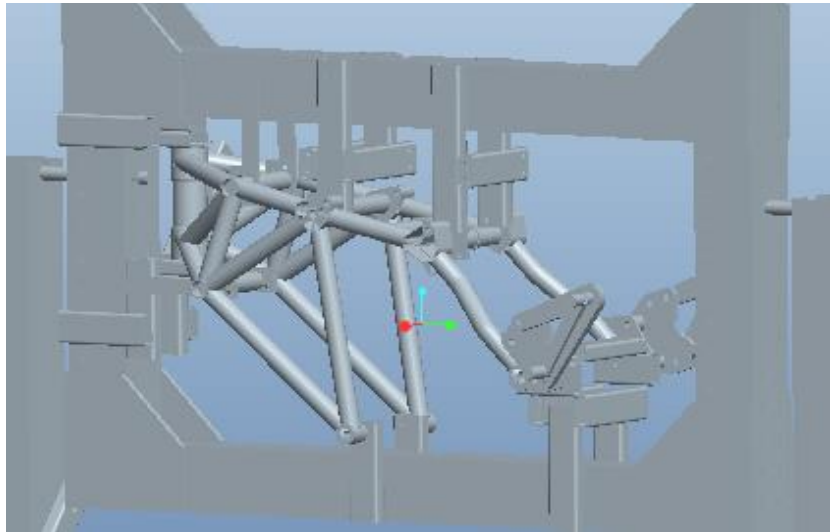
Diseño del potro de soldadura al completo para el chasis
